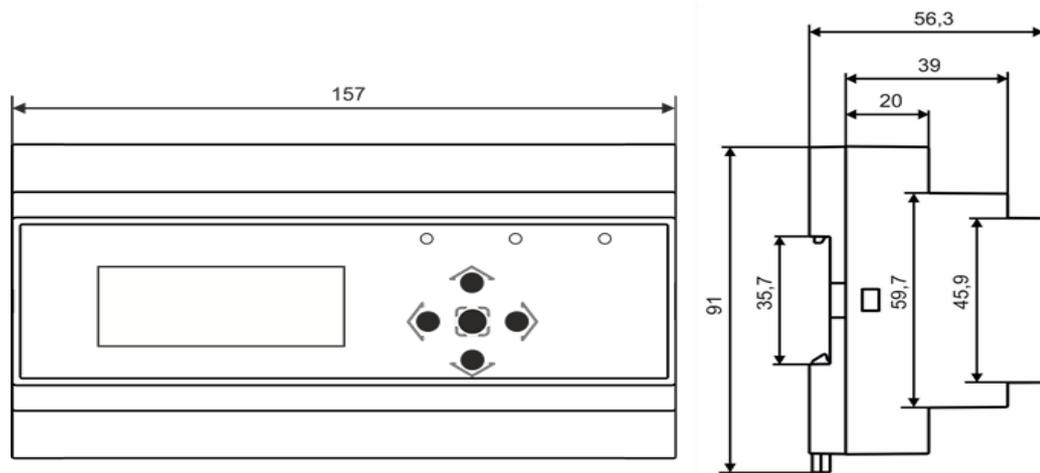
Габаритні та установчі розміри RPM-416
